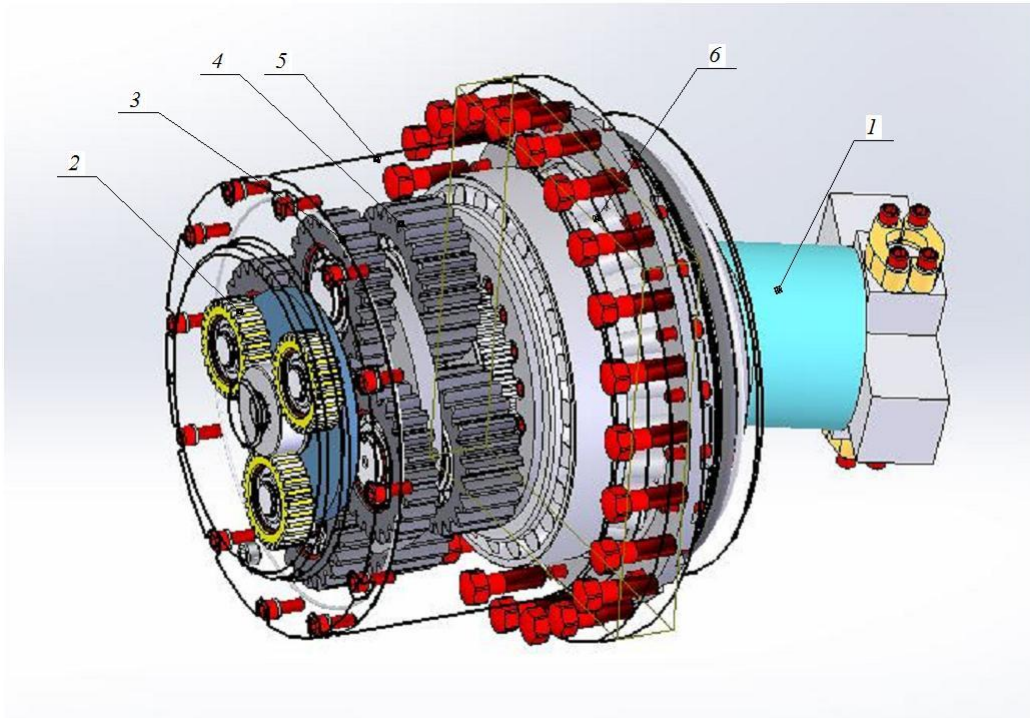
Редуктор механизма передвижения: 1 – гидромотор; 2 – быстроходная ступень; 3 – промежуточная ступень; 4 – тихоходная; 5 – корпус; 6 – тормоз
